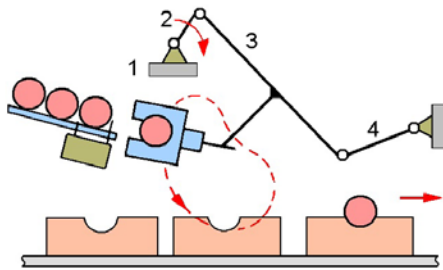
Getriebetechnische Lösung für eine Teilezuführung.
